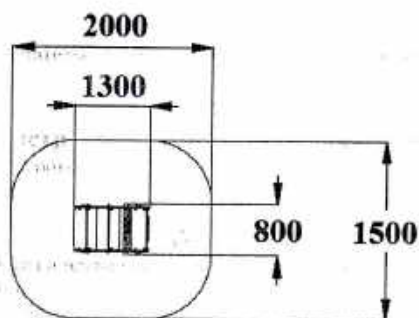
Габаритные размеры изделия. Размеры площадки для установки.
